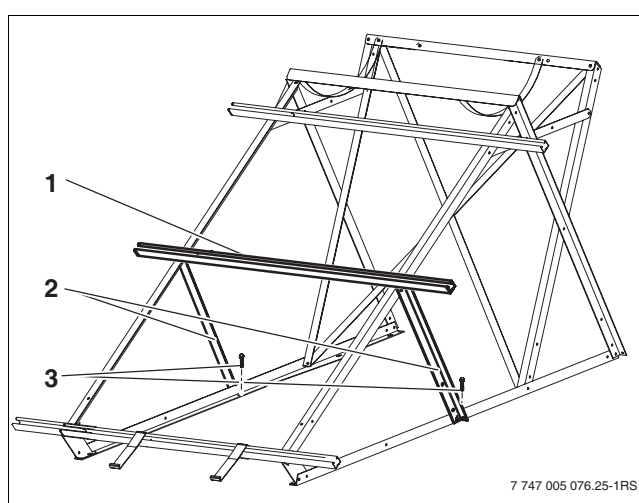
Apoios adicionais para o sistema de telhados planos (aqui, no sistema de 150/200 I)
